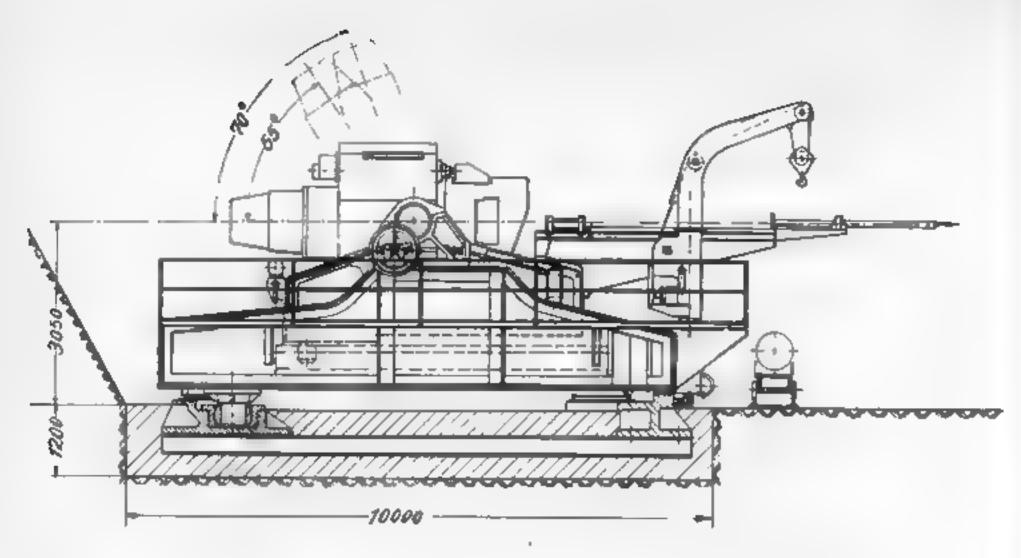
Einbau auf Unterlafette mit Rucklauf auf Betonfundament
